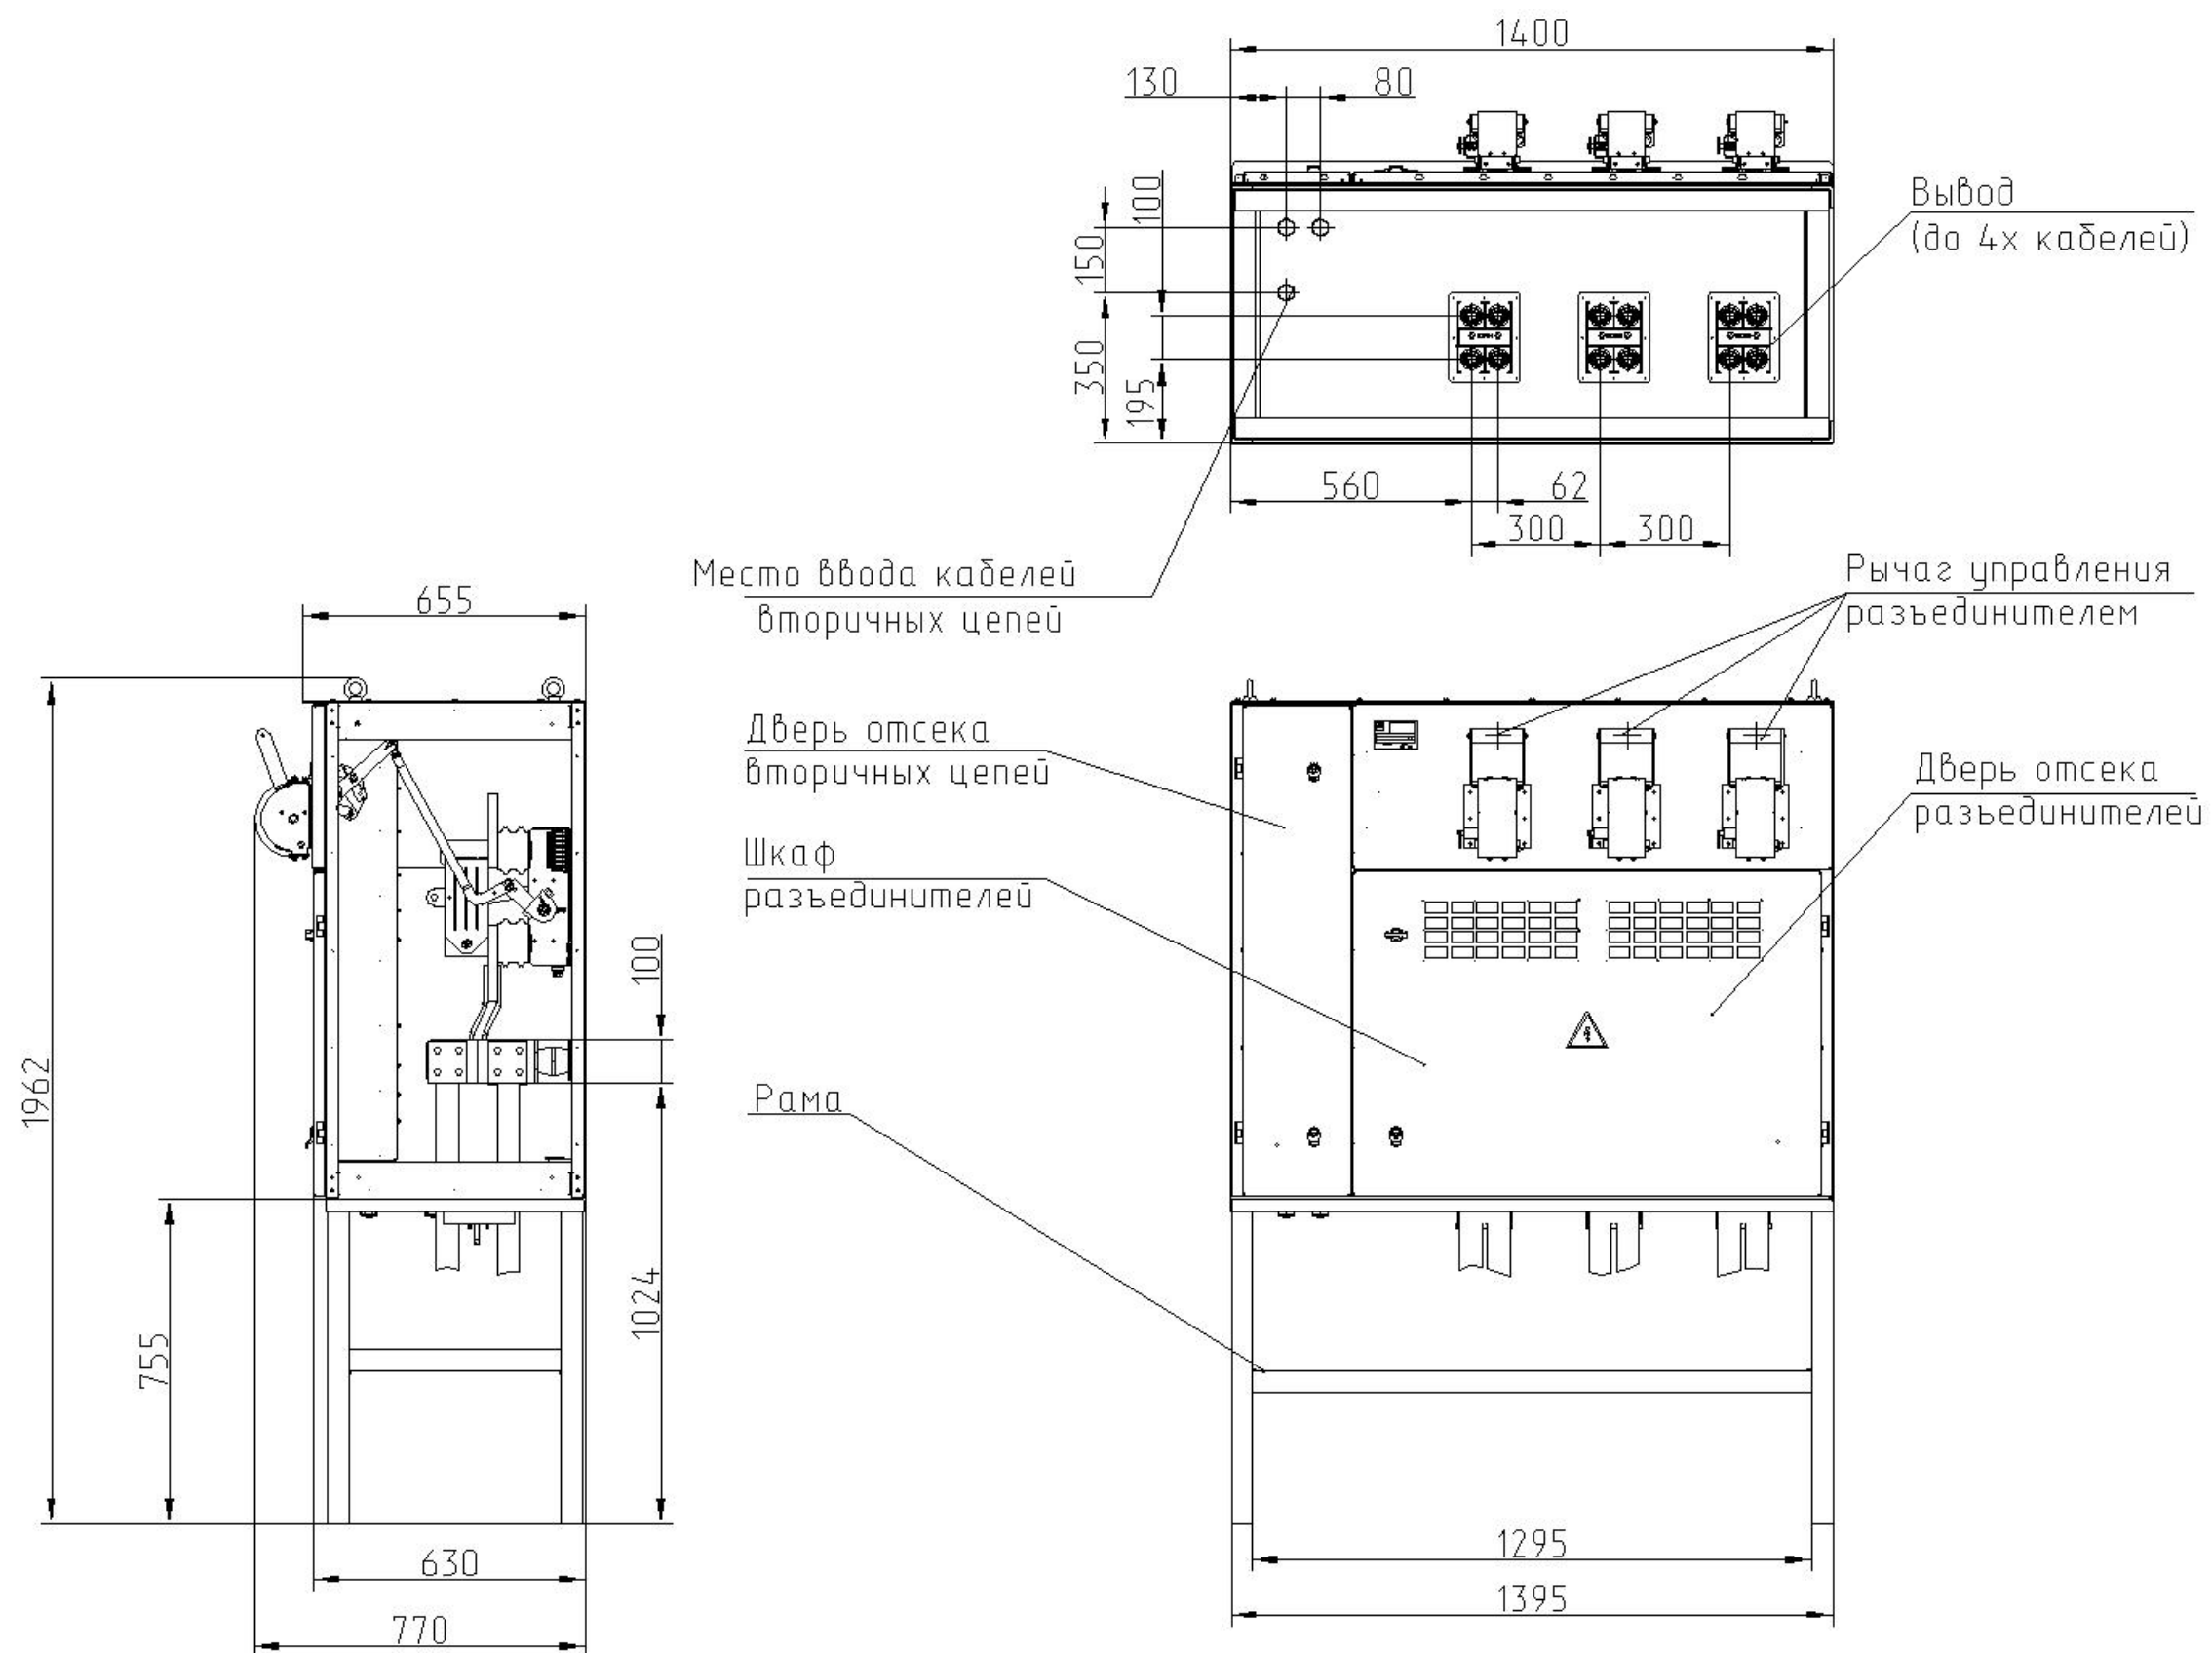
ПРД-825-3-У1, с ручным приводом разъединителя
